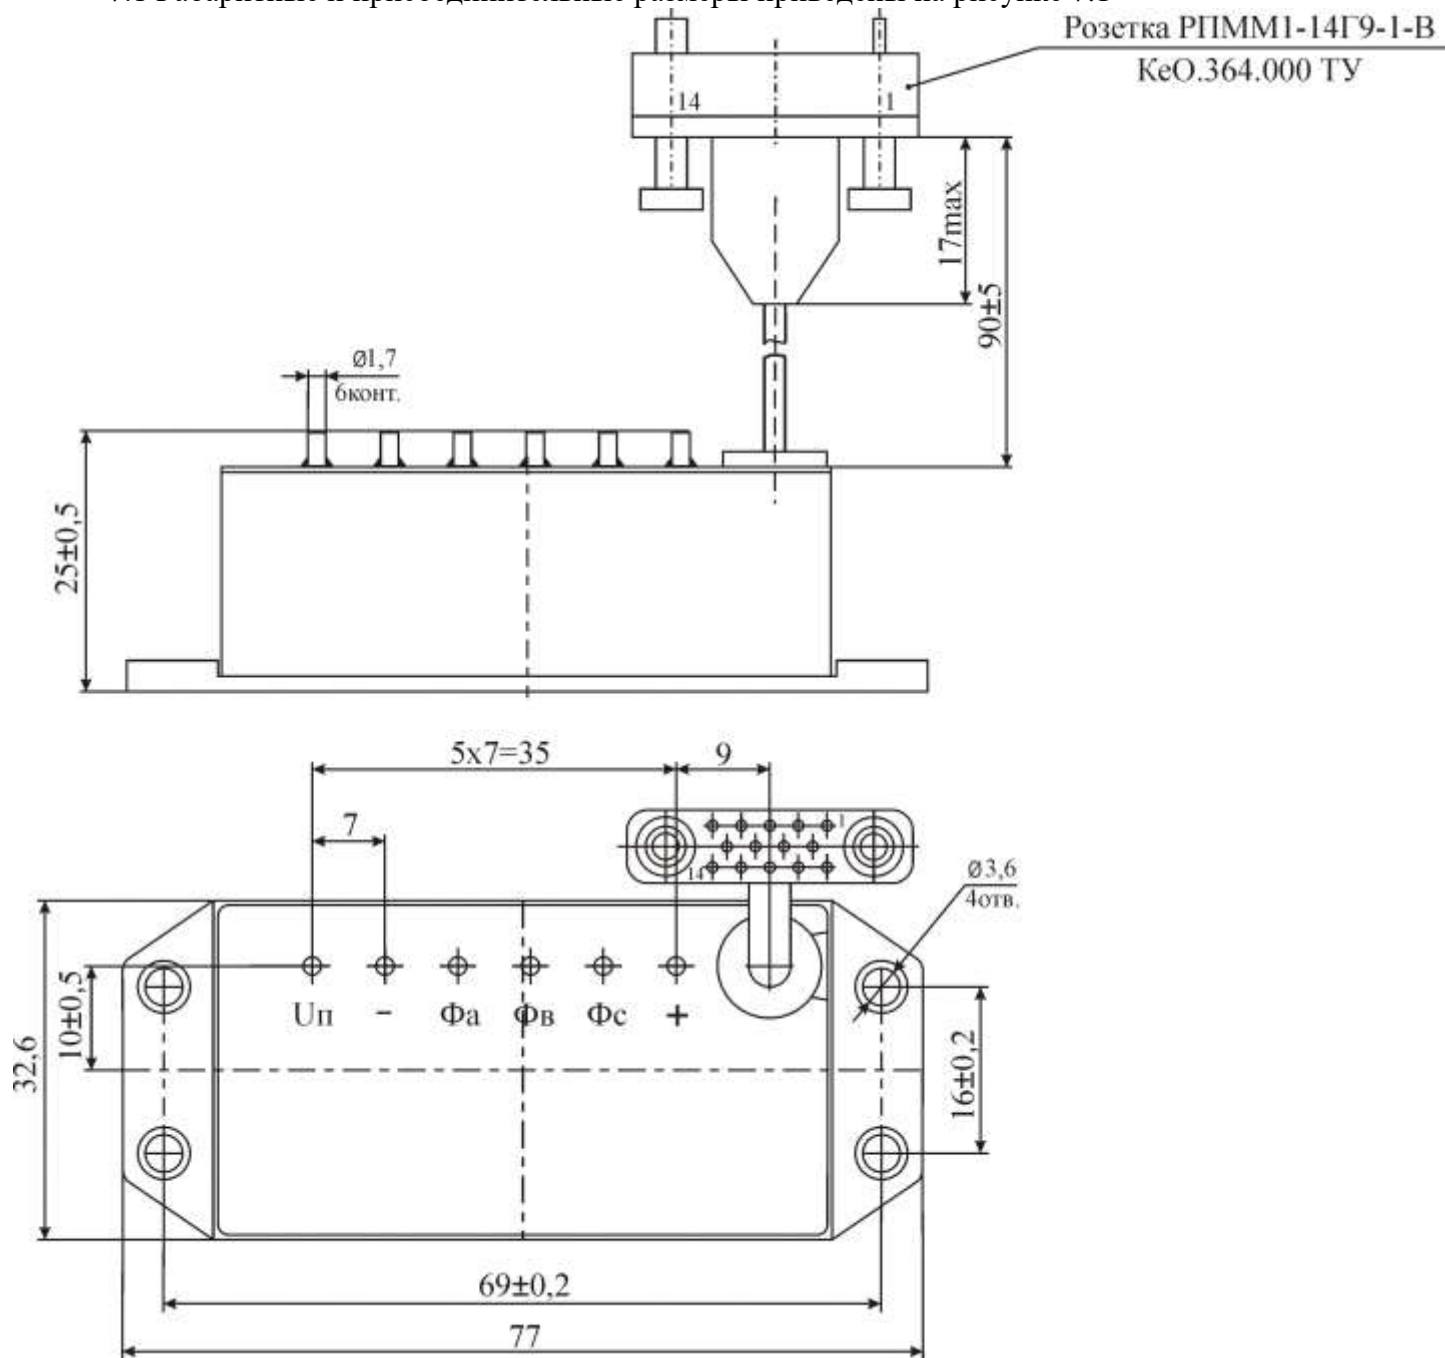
Габаритные и присоединительные размеры 5УМ14А
